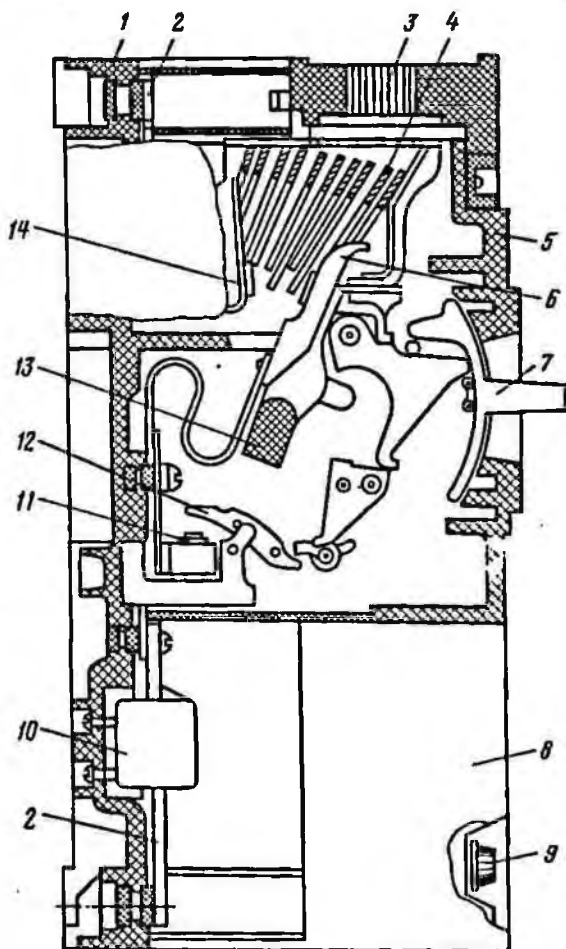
Схематичное устройство автоматического воздушного выключателя А-3700
